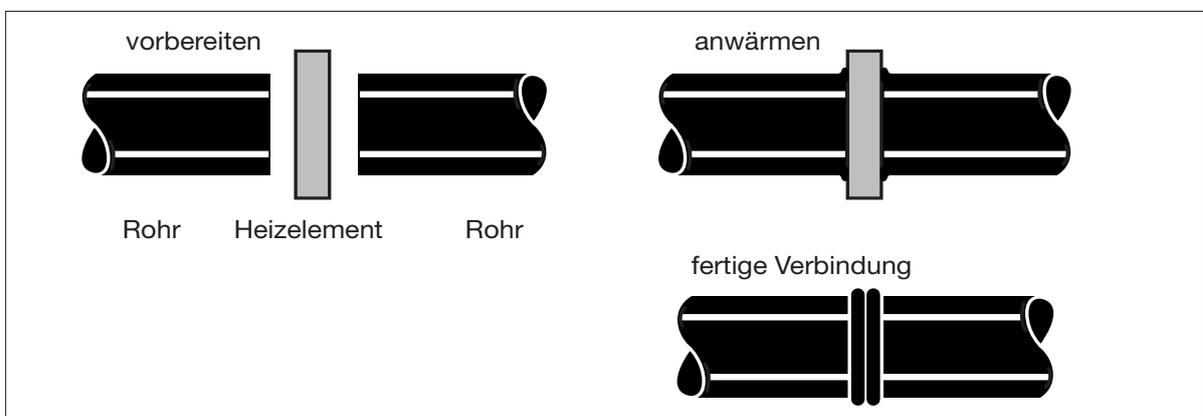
Prinzip der Heizelement-Stumpfschweissung
